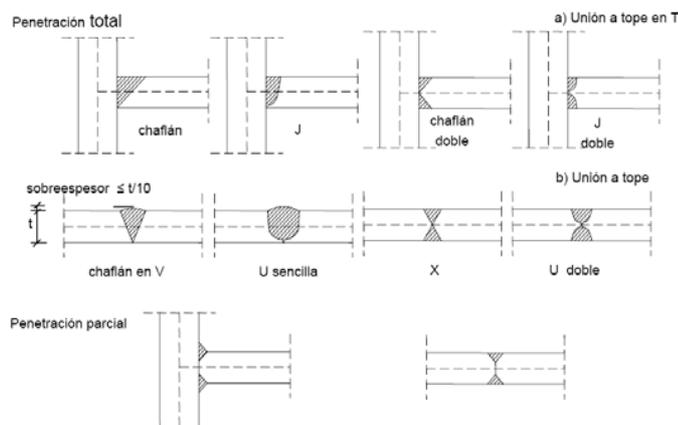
Soldadura a tope y formas de preparación
